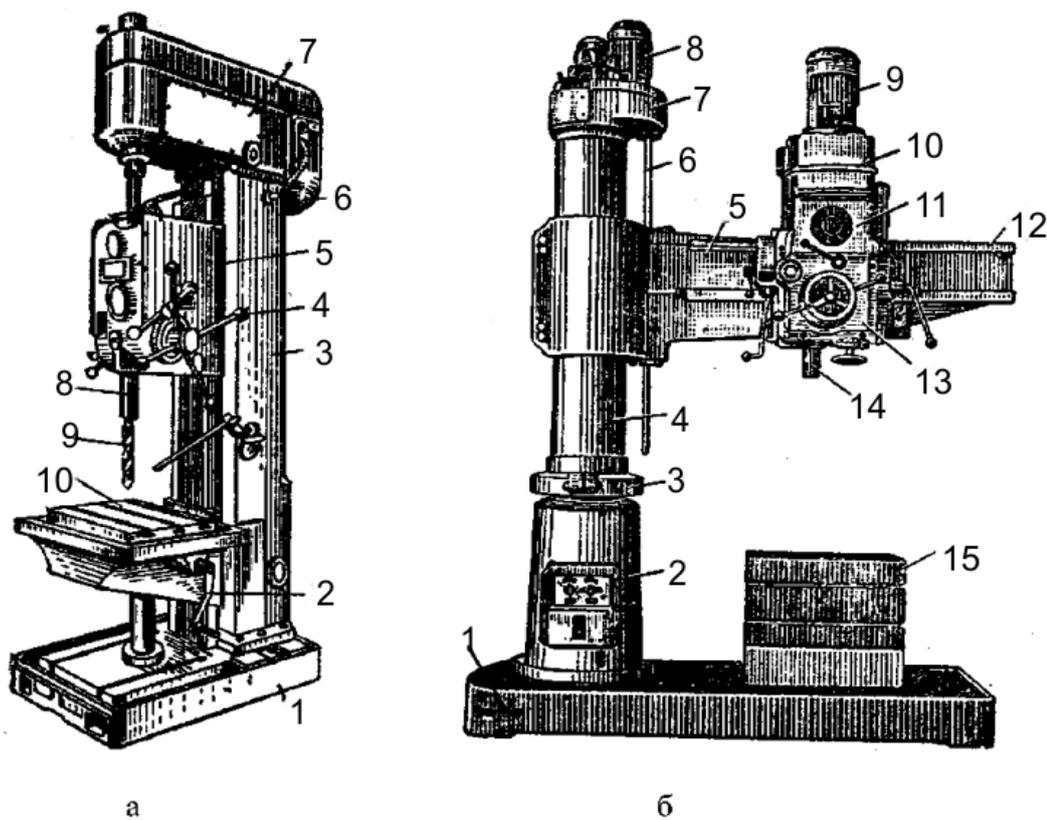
Одношпиндельный вертикально-сверлильный станок
